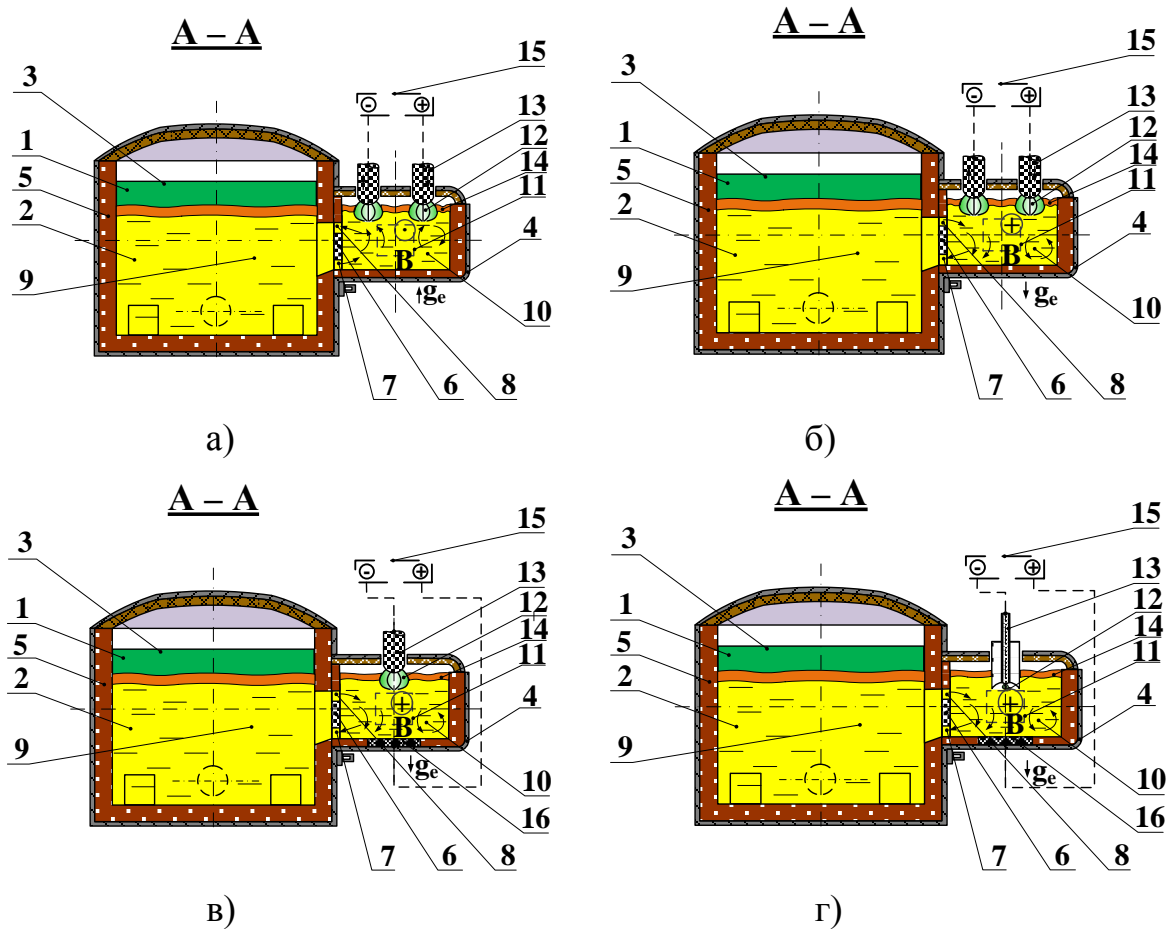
Разрез A – A промежуточного ковша с различными схемами нагрева и обработки расплава: а, б – нагрев двумя сводовыми электродами с электромагнитным облегчением и утяжелением расплава для его циркуляции соответственно; в – одноэлектродный нагрев с токоподводящим подовым электродом, и циркуляция расплава за счет электромагнитного утяжеления; г – нагрев, раскисление-легирование и рафинирование расплава заглубленным ДБ, и циркуляция расплава за счет электромагнитного утяжеления
